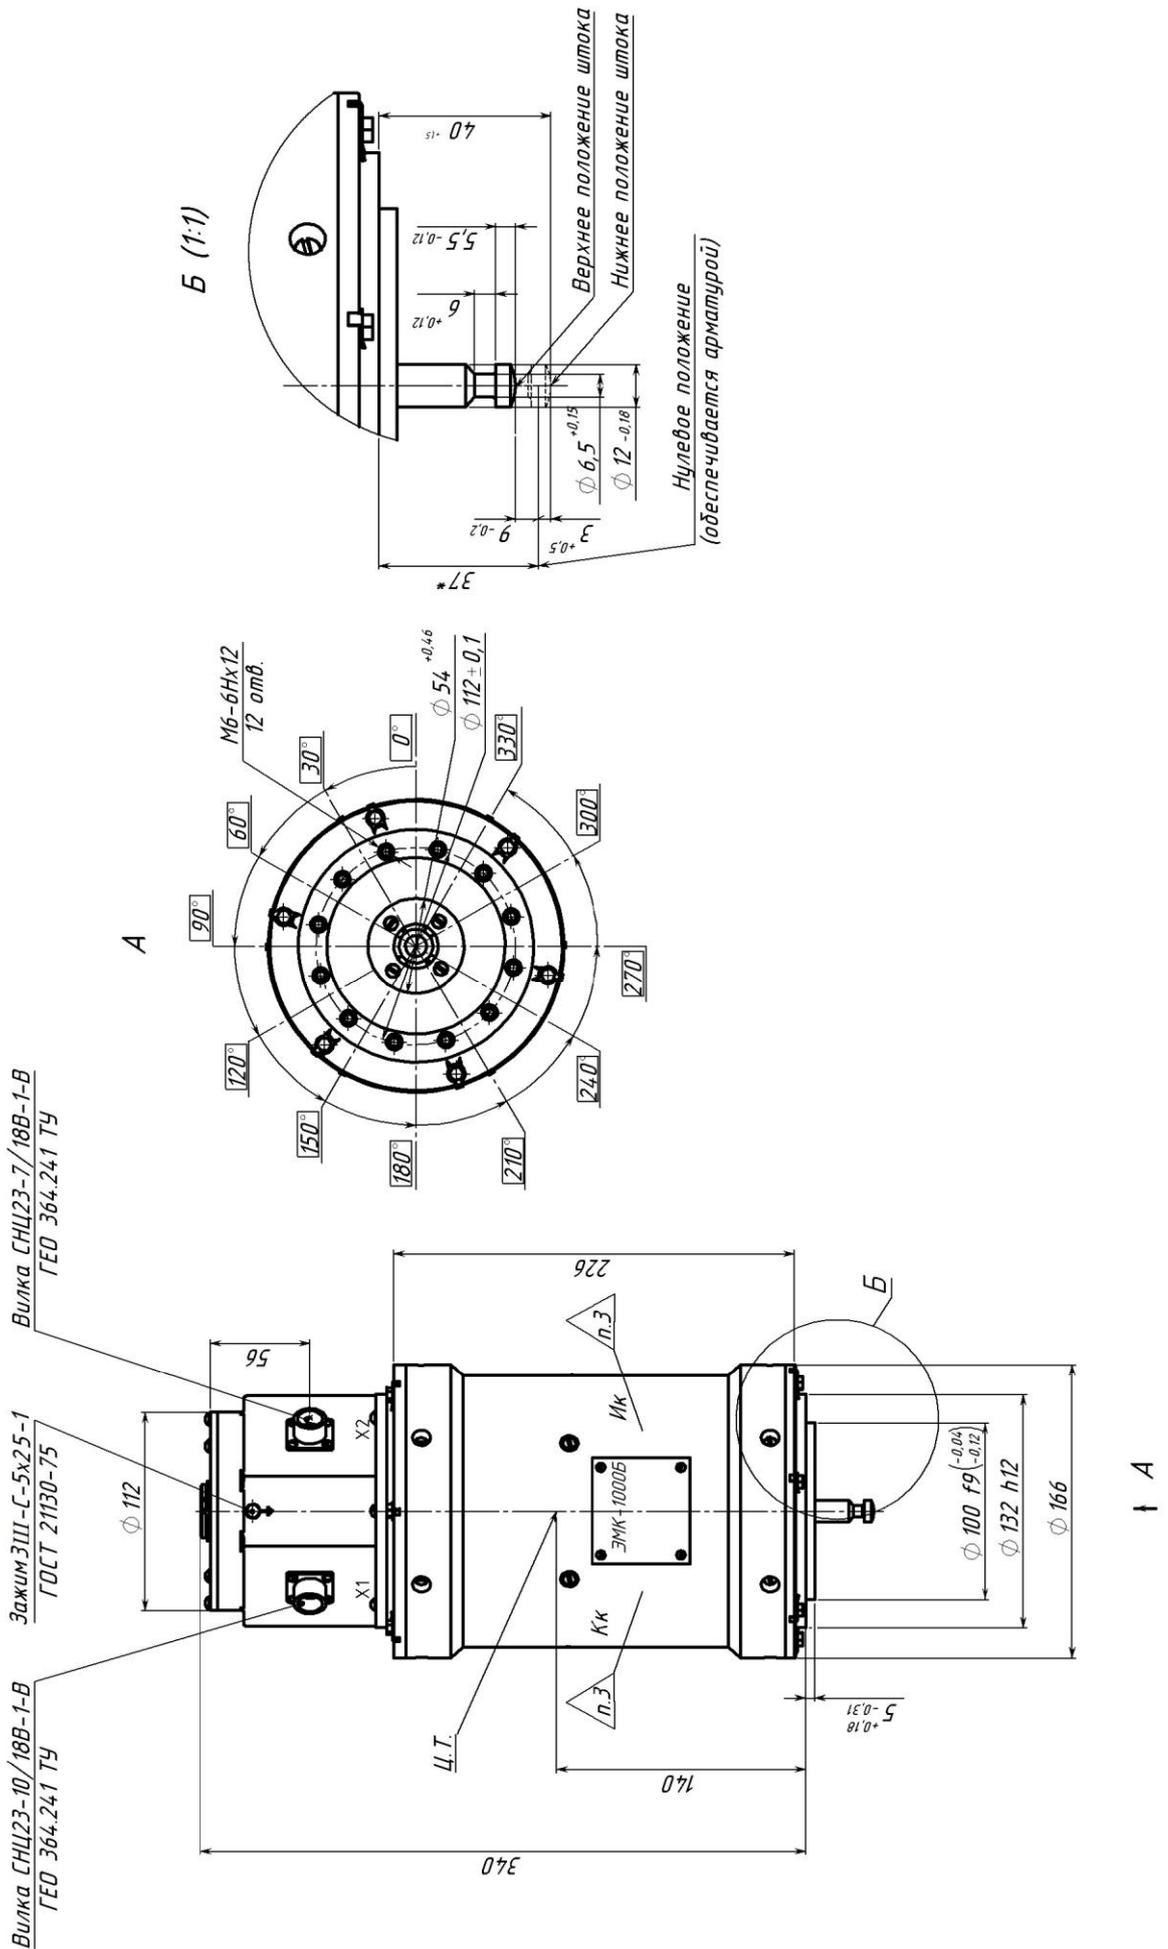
Габаритный чертеж привода ЭМК1000Б
